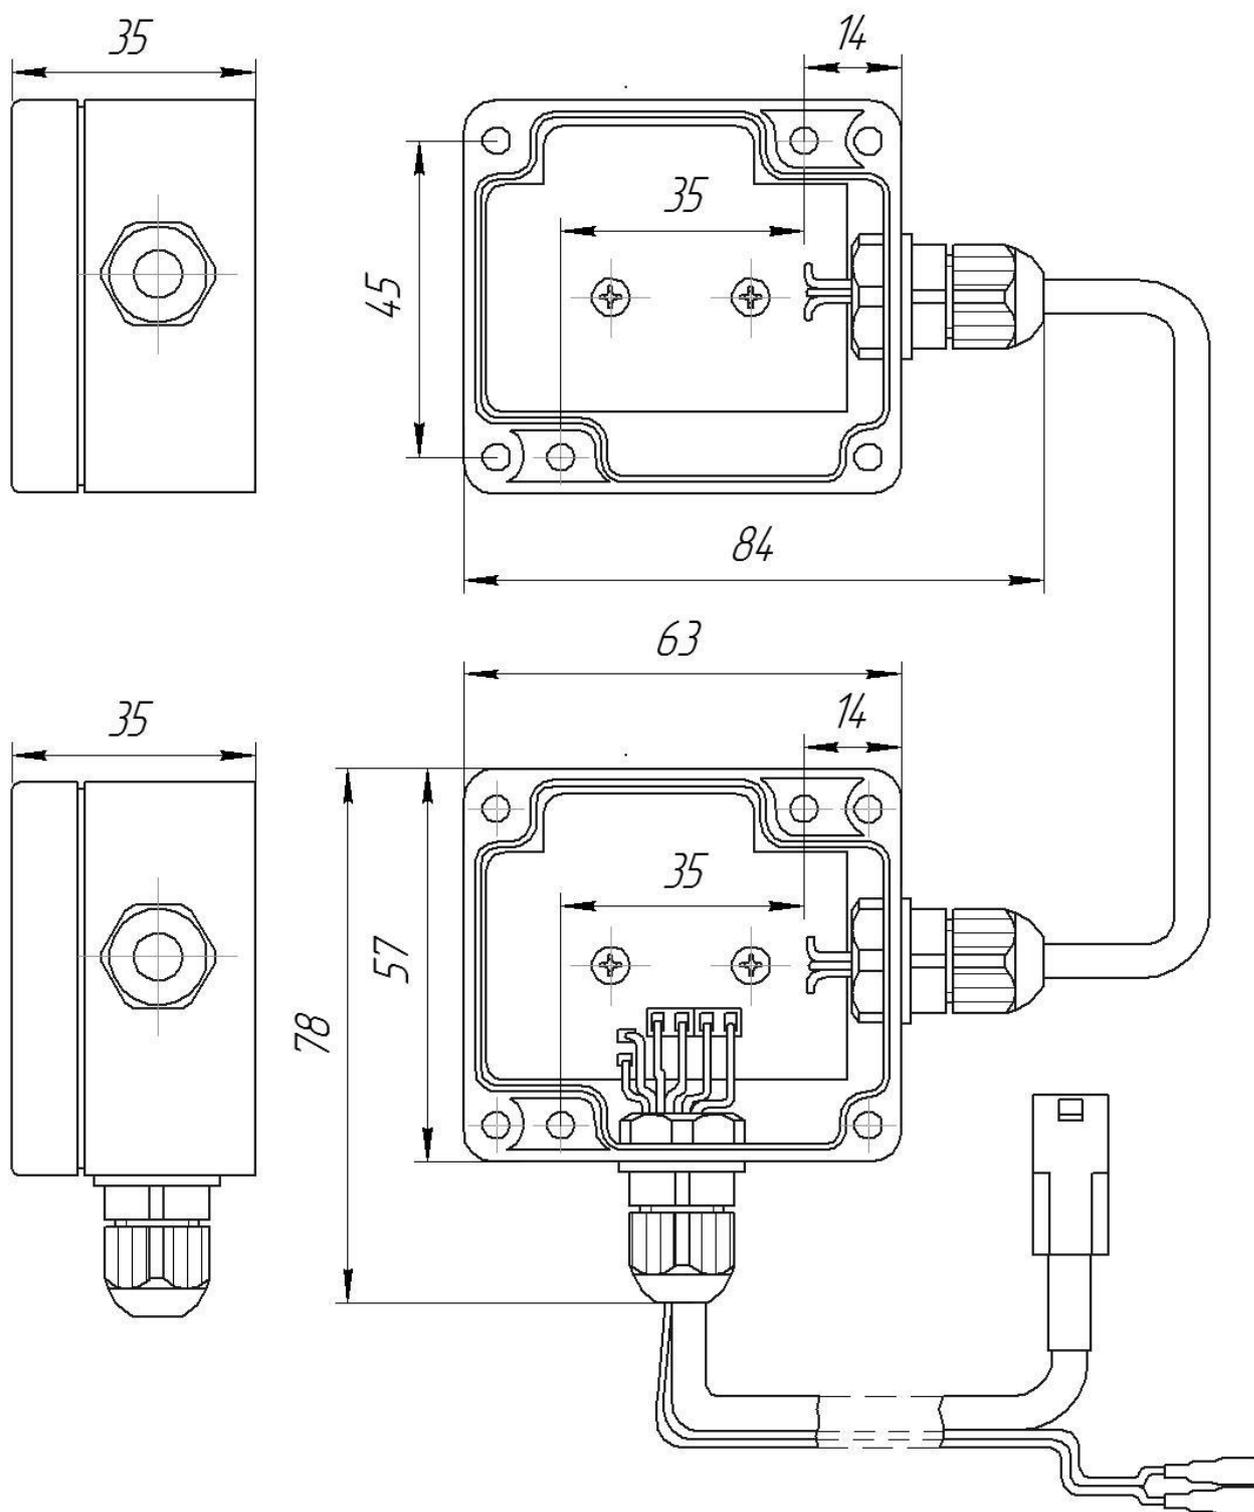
Габаритные и присоединительные размеры ИК-датчика «Луч-МС».
